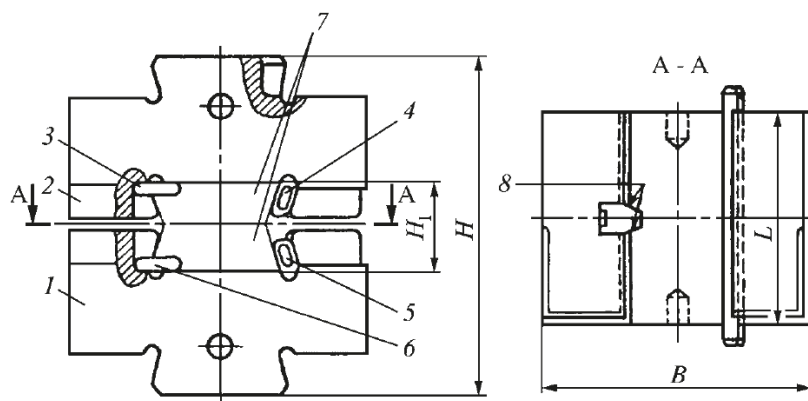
Блоки универсальные молотовых штампов с призматическими вставками [2]: 1 — нижний блок; 2 — верхний блок; 3 — верхняя шпонка; 4 — верхний клин; 5 — нижний клин; 6 — нижняя шпонка; 7 — призматические вставки
